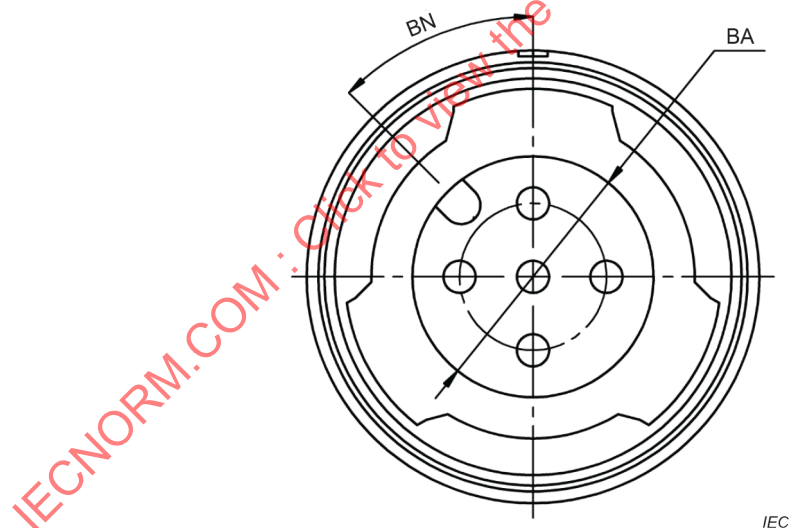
Vue de face du côté femelle du boîtier de type pousser-tirer pour le codage A
